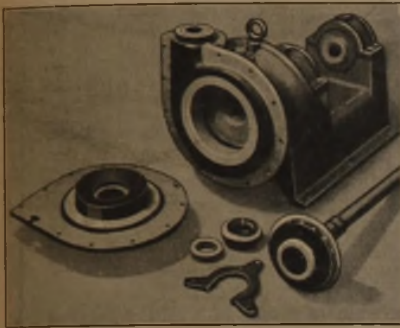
Kreiselpumpe aus Steinzeug für Säuren und Laugen.
